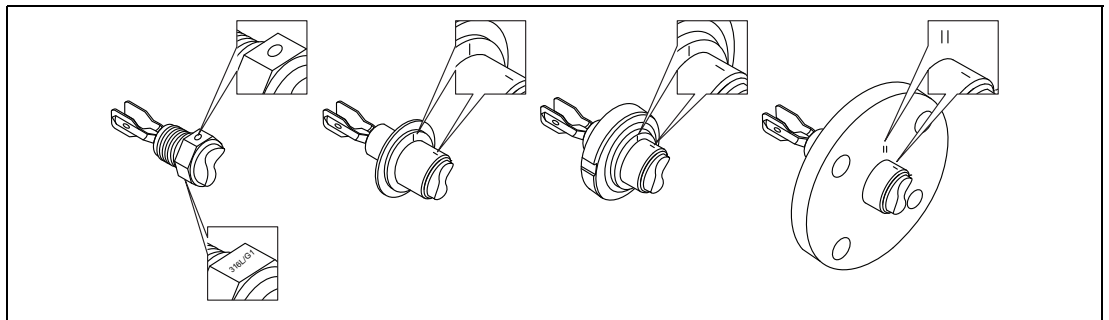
Markierungen für die Ausrichtung der Schwinggabel
